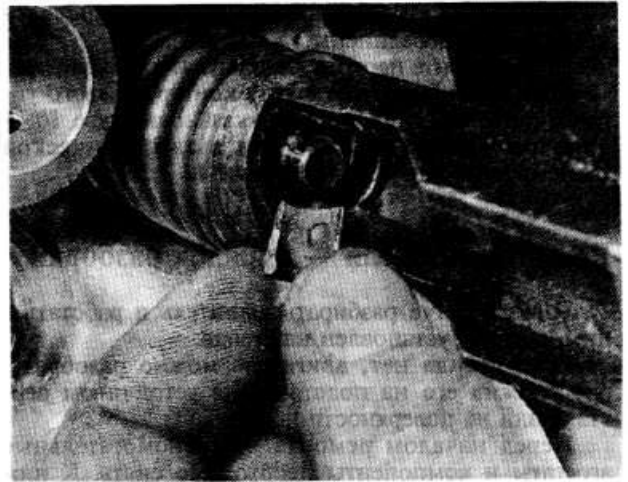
Извлечение сухой клапана — двигатель с одним распредвалом
